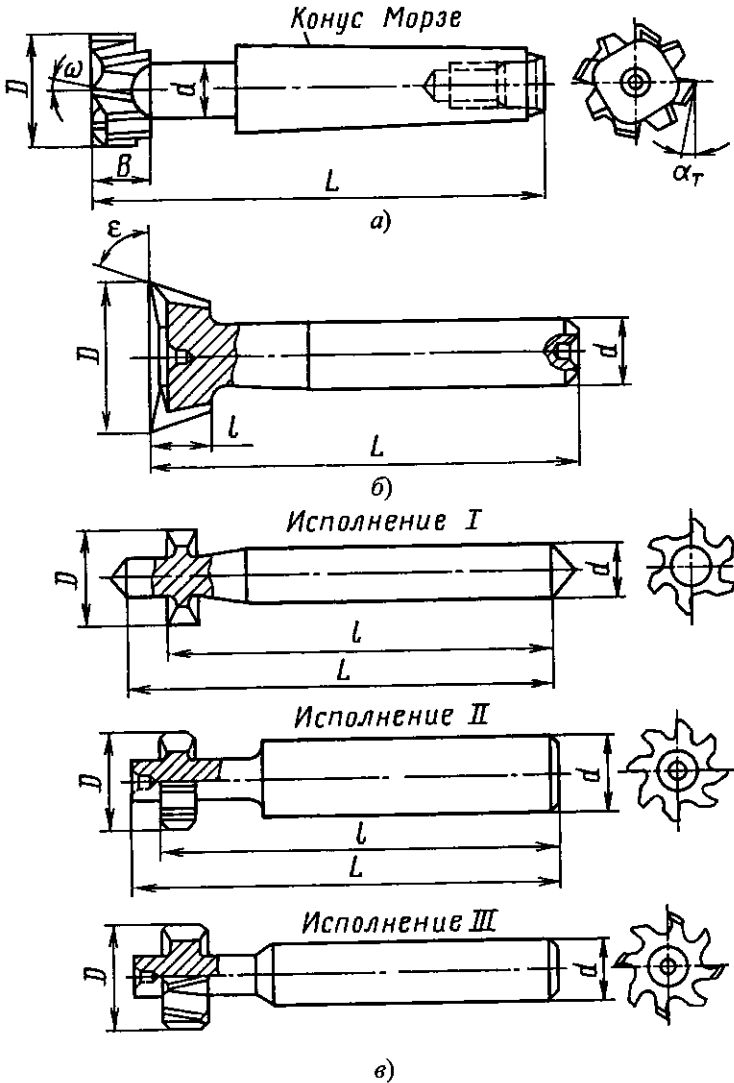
Фрезы для обработки пазов: а – станочных Т-образных; б – типа "ласточкин хвост"; в – под сегментные шпопки
